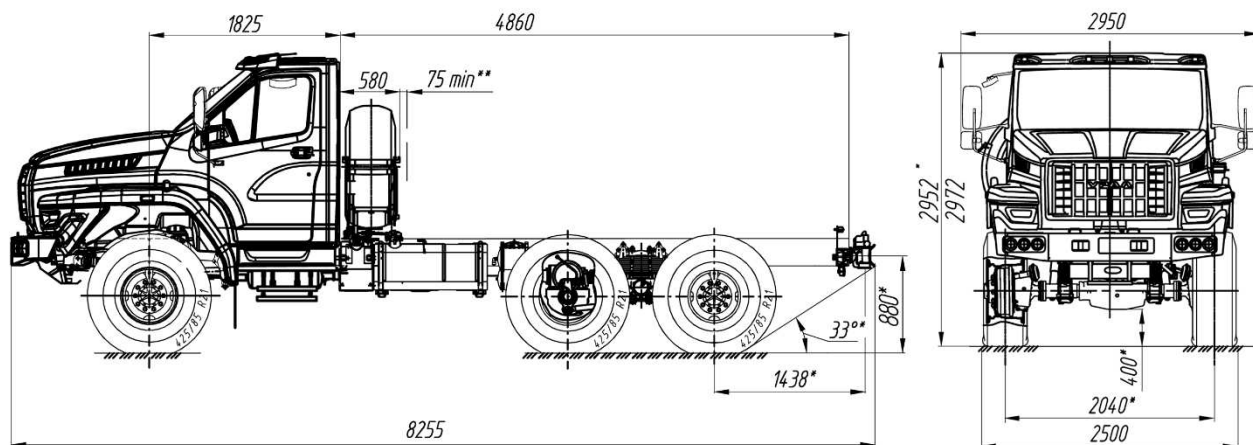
Габаритные размеры шасси Урал-5557-6151-72/74
